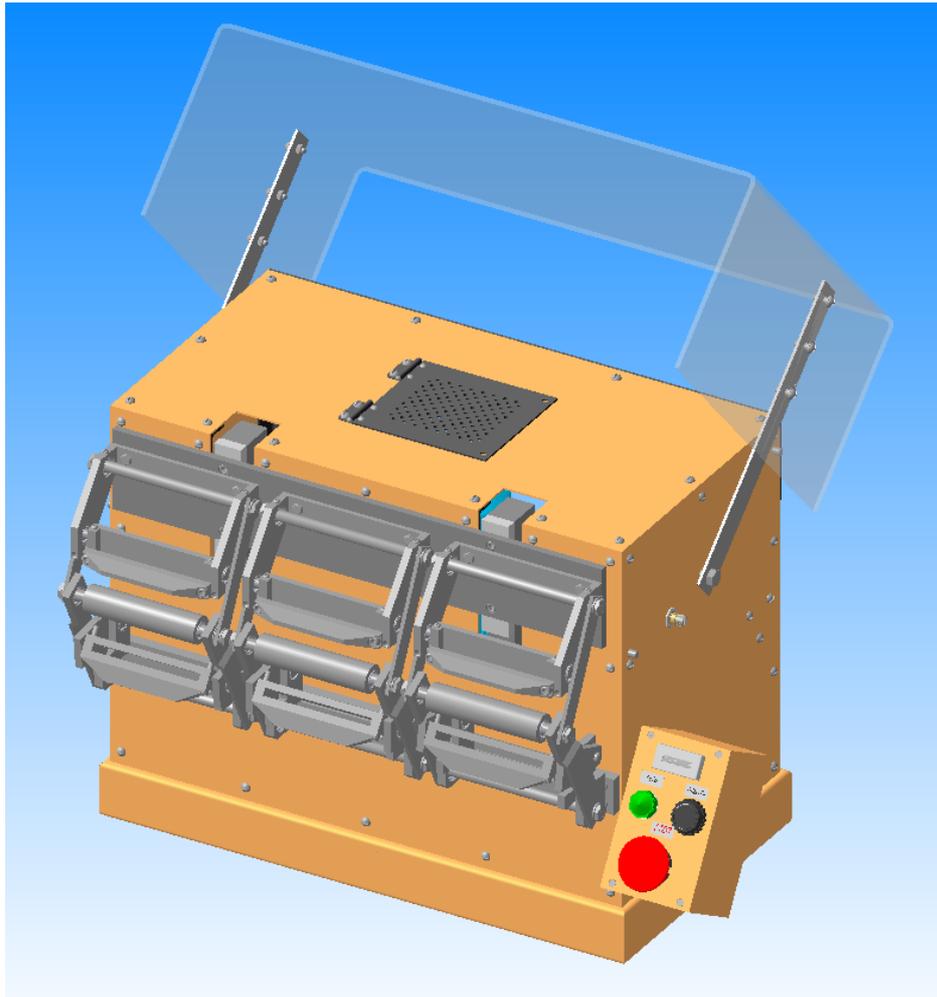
Внешний вид разработанной 3D-модели установки
